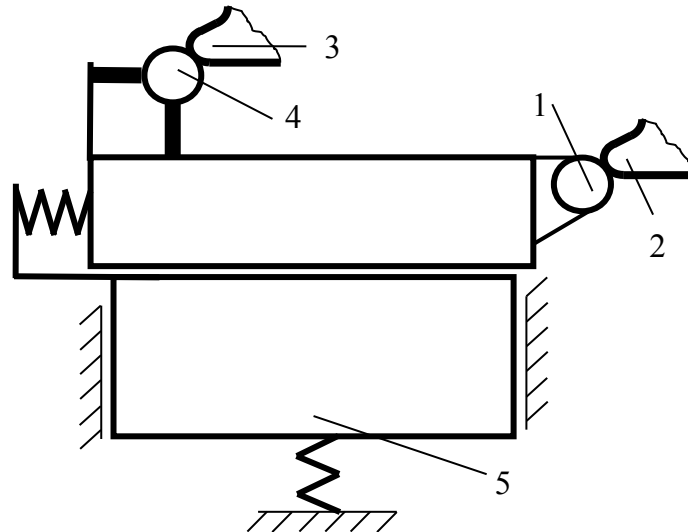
Схема утворення динамічної погрішності при обробці фасонної поверхні залізничного колеса по копіру: 1 - інструмент; 2 - оброблюване залізничне колесо; 3 - копір; 4 - електроконтактний щуп; 5 - копіювальний супорт
